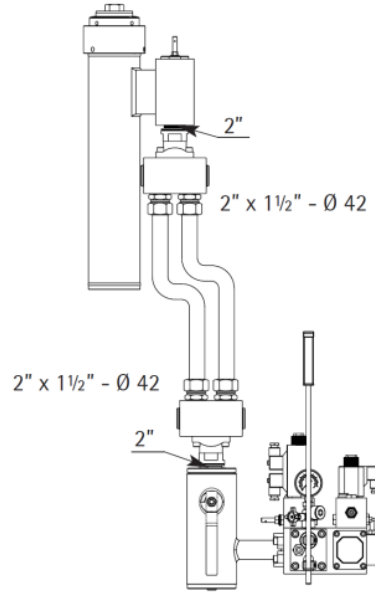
Collegamento con n°2 Tubi rigidi Ø 42
